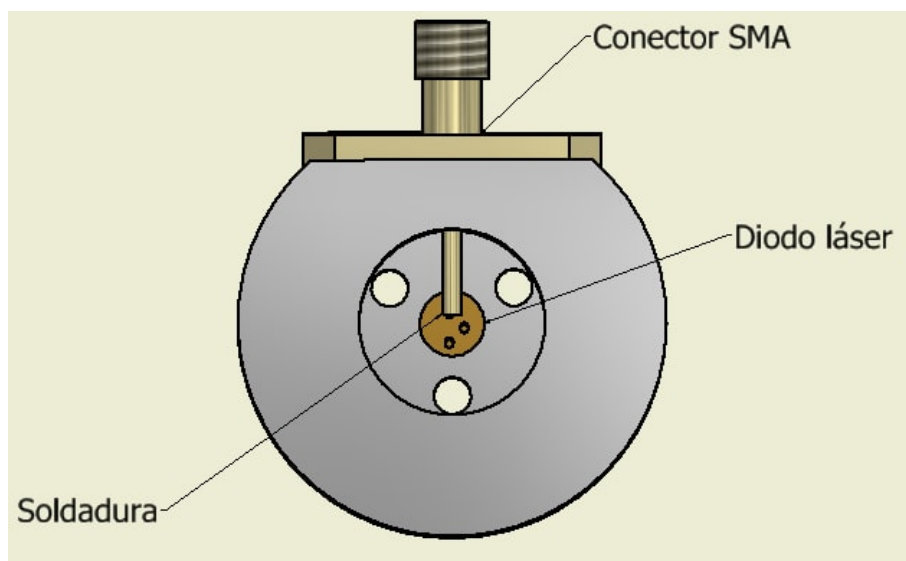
Vista trasera de la montura principal con el conector SMA y el diodo láser colocados. En la figura se indica el lugar de la soldadura de la terminal que lleva la señal en el SMA con el ánodo del diodo láser.
